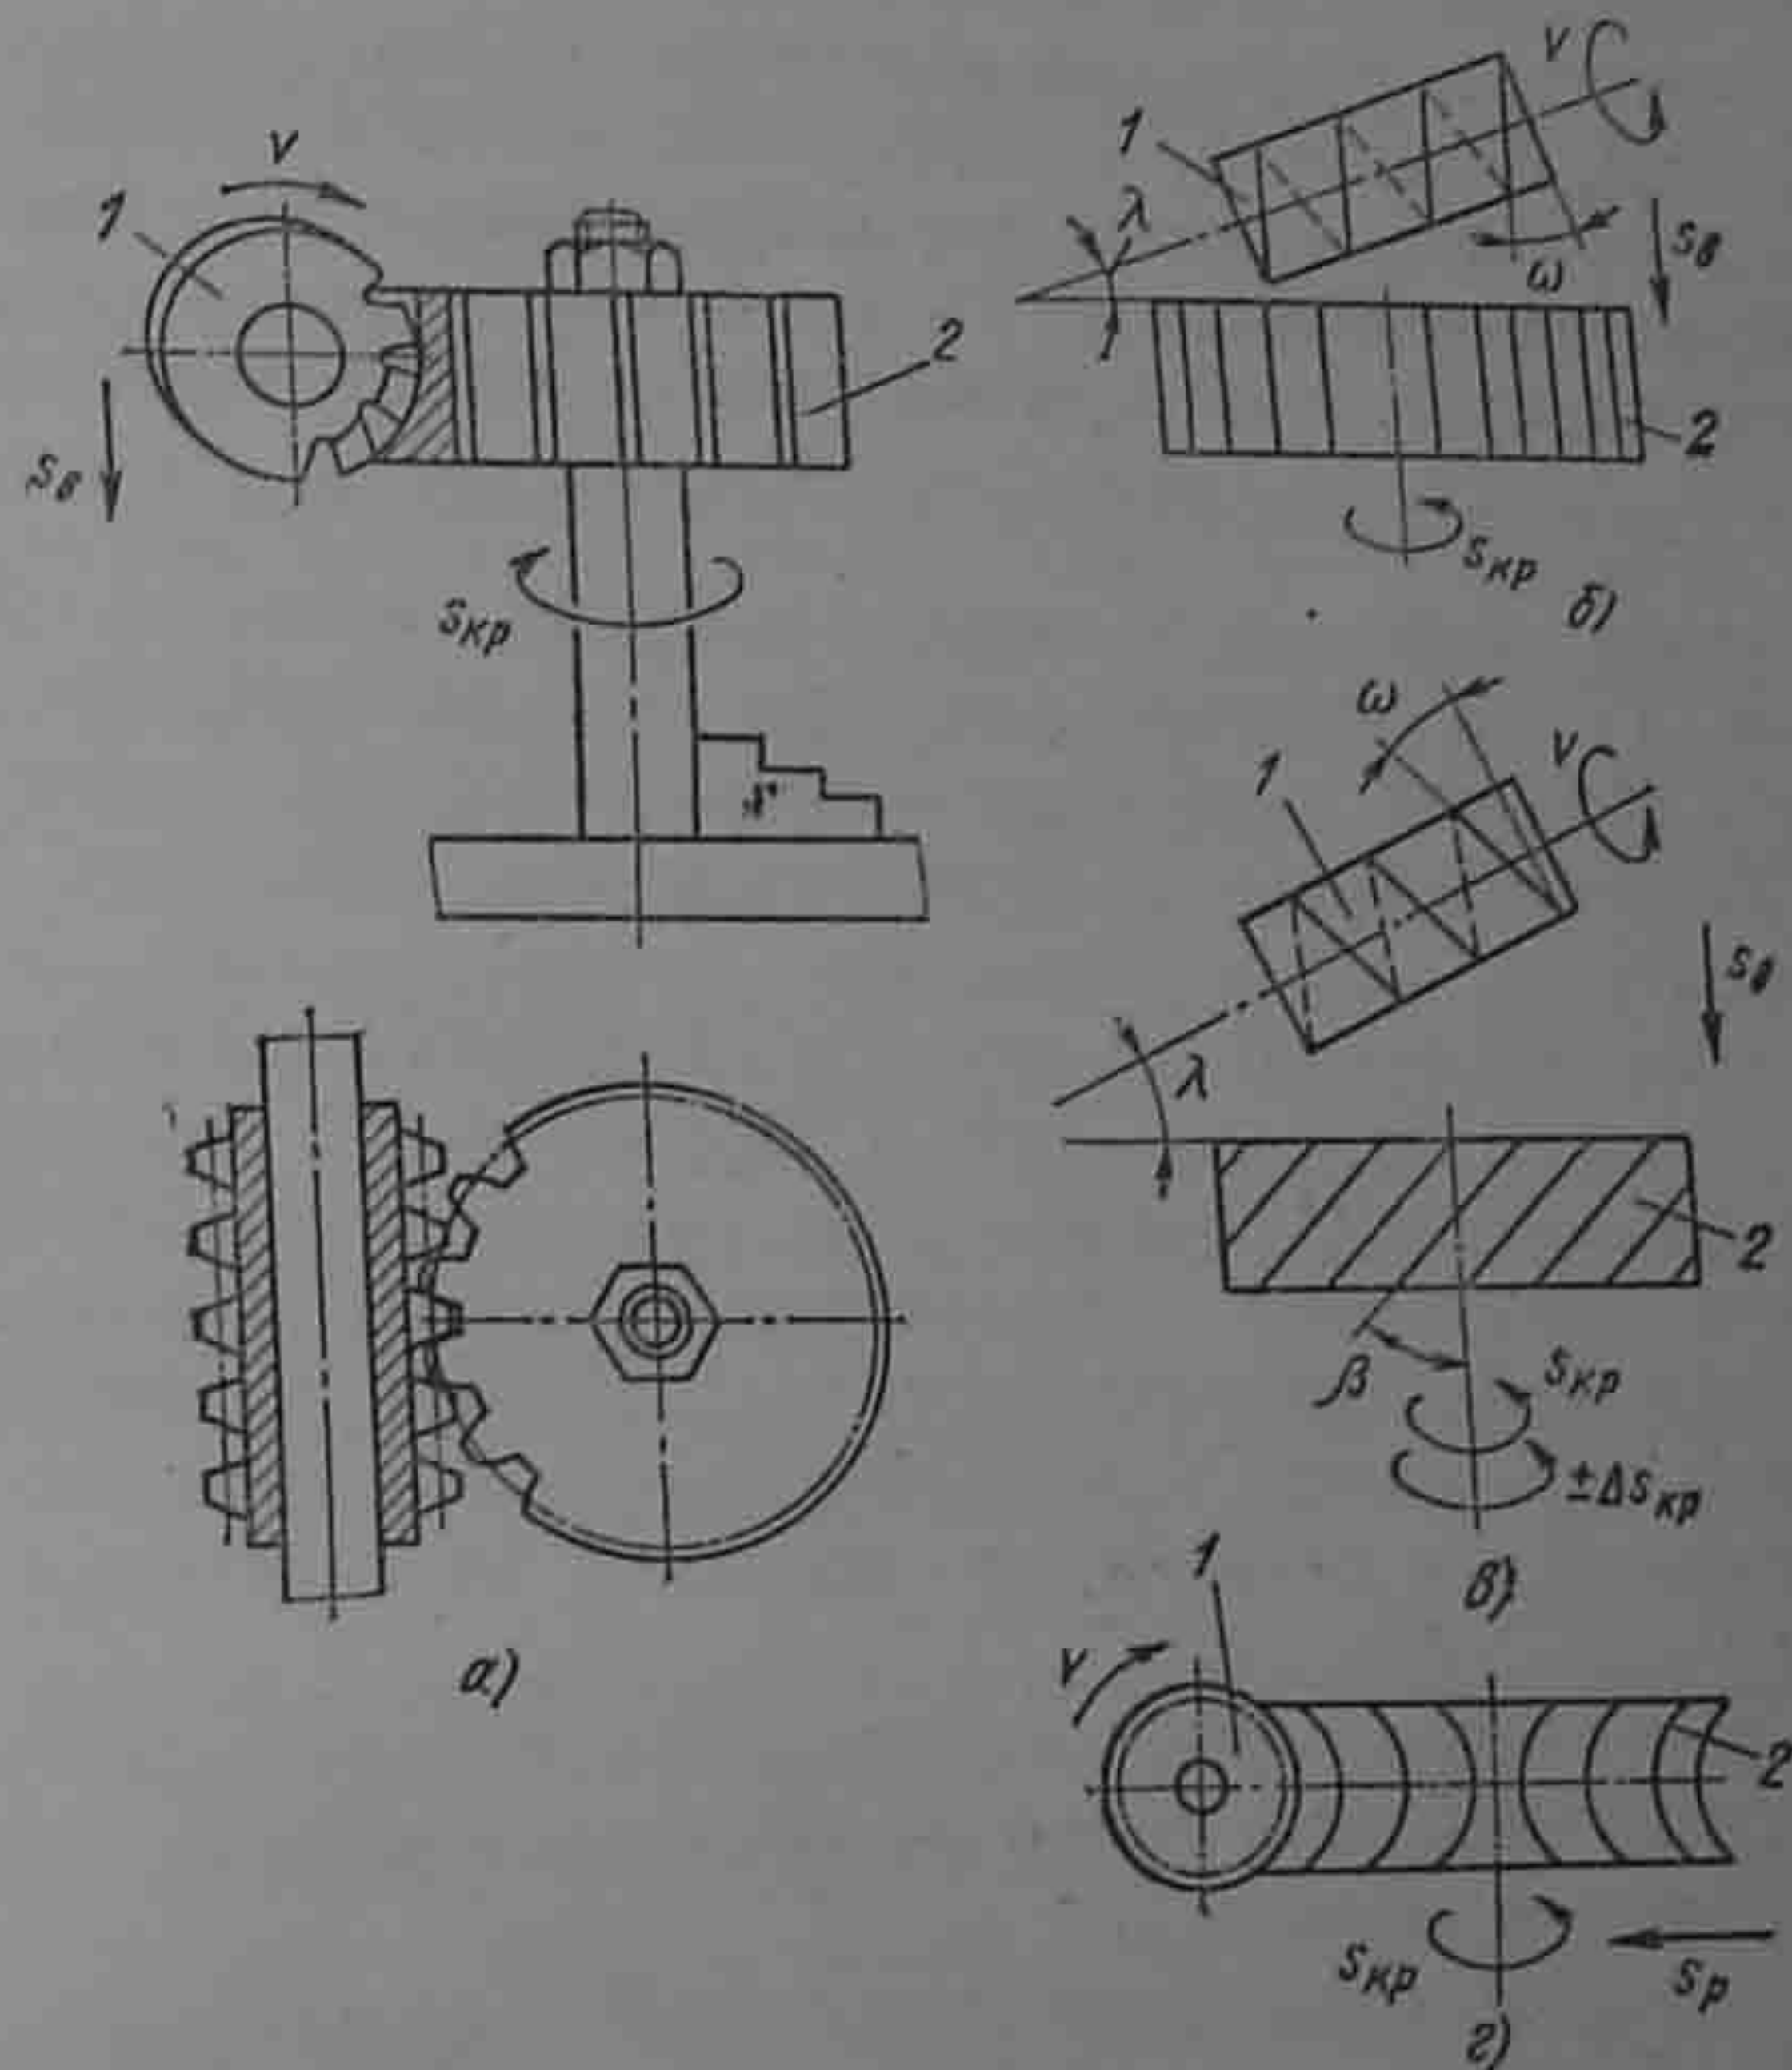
Схемы нарезания цилиндрических зубчатых колес на зубофрезерном станке:
